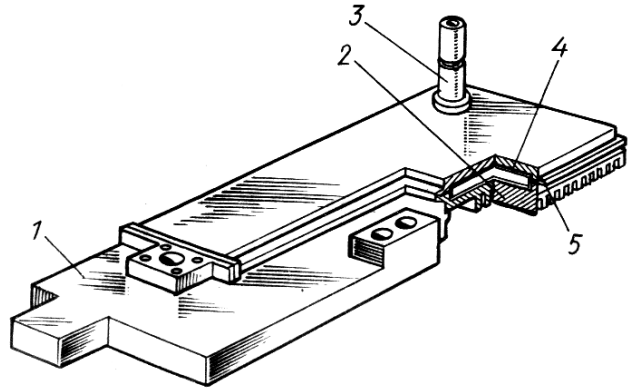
Корпус узла РЭС с тепловой трубой: 1—корпус РЭС; 2—радиатор; 3—откачной штенгель; 4—фитиль; 5—место пайки двух половин корпуса тепло-
